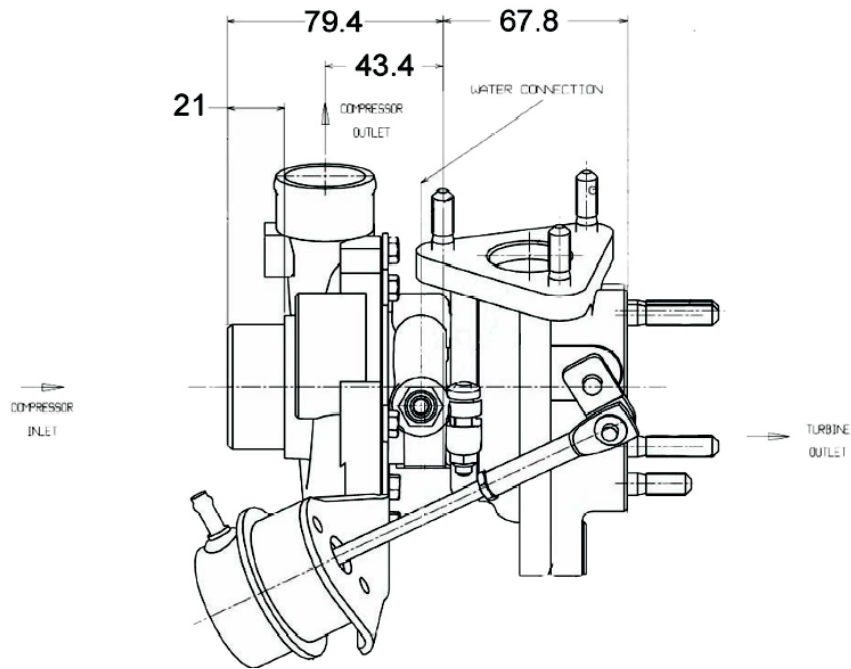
23 Dimensiones del Turbocompresor Seleccionado.
